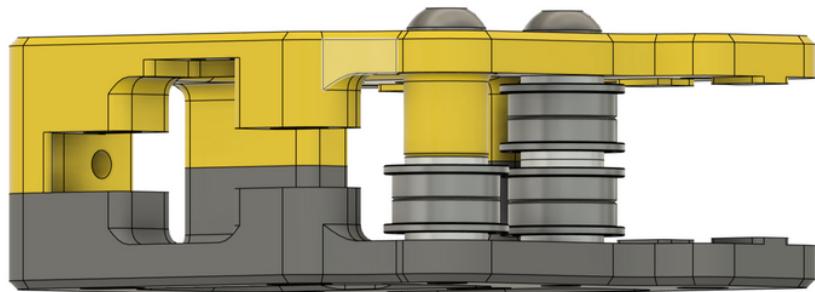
Vista completa del tensor trasero con los componentes ensamblados.
